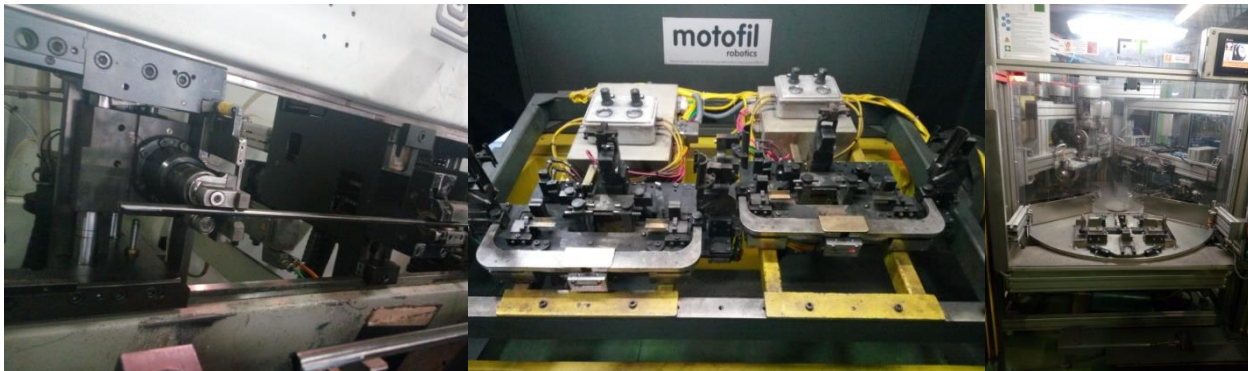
Célula HAB01, Máquina dobrar tubo BLM VGP (esquerda), gabaritos soldadura (centro), Máquina de corte e rebarbagem de tubo Fluidotróica (direita)
